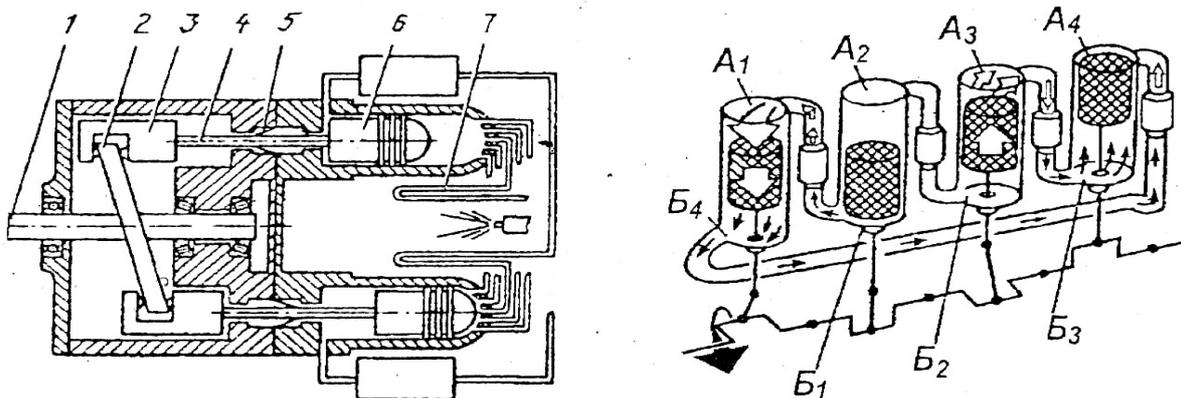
Двигатель Стирлинга фирмы «Форд»: а) конструктивная схема; б) схема работы двигателя
